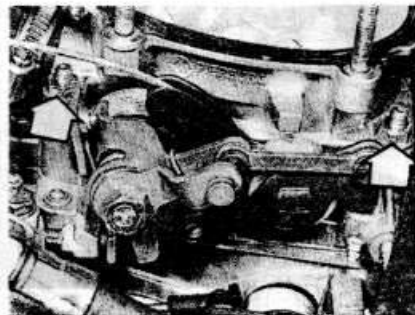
Две гайки крепления корпуса дросселя — система впрыска топлива Motronic M2.5
